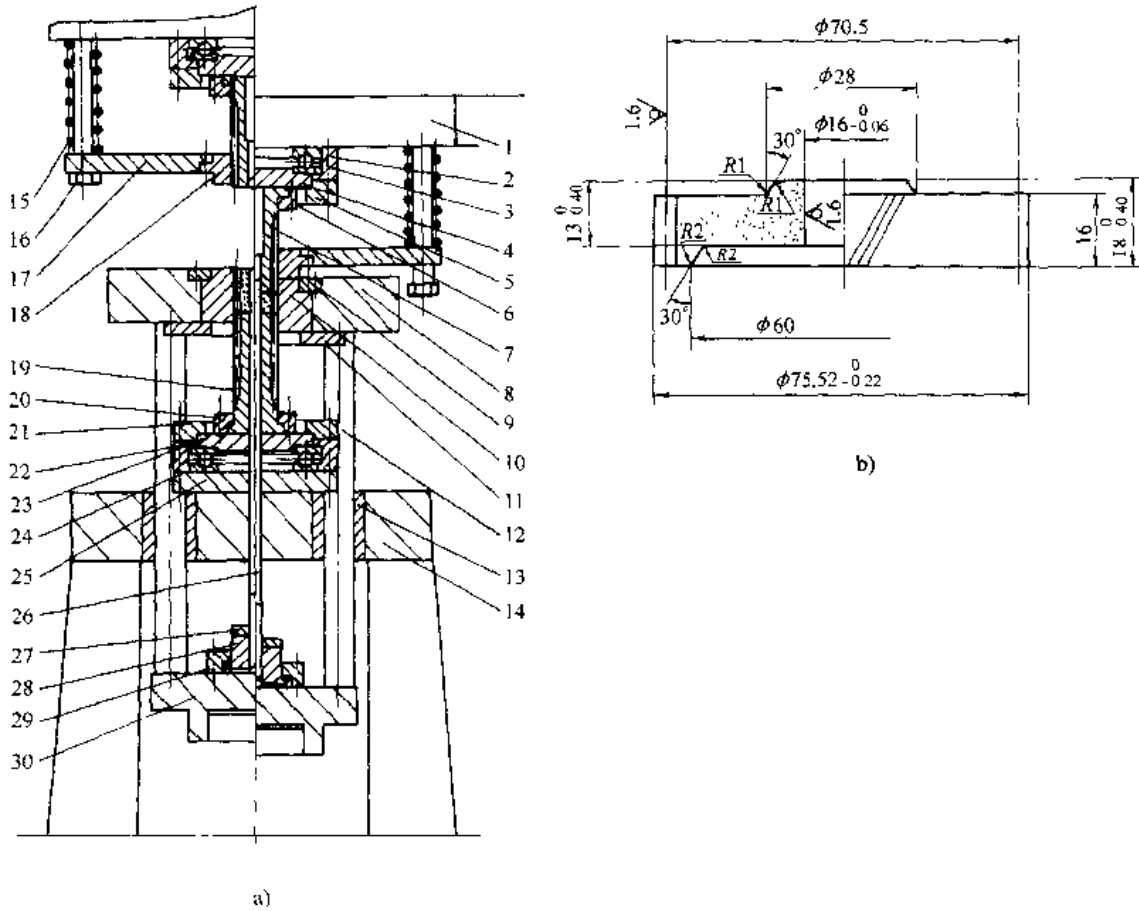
电动工具变速器斜齿轮压坯的成形模具
